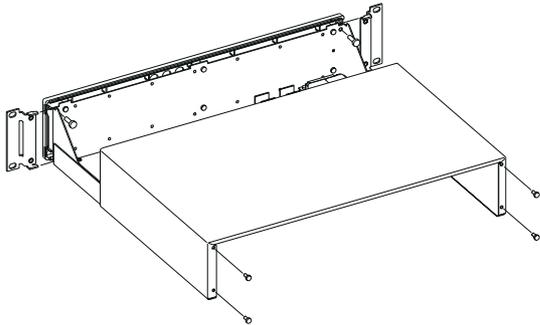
Cómo retirar la cubierta y las orejetas de montaje en estantería
